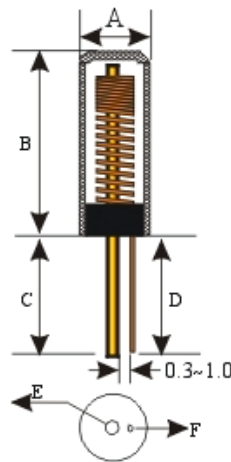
Layout sensor de vibración empleado. M&M (2013).
